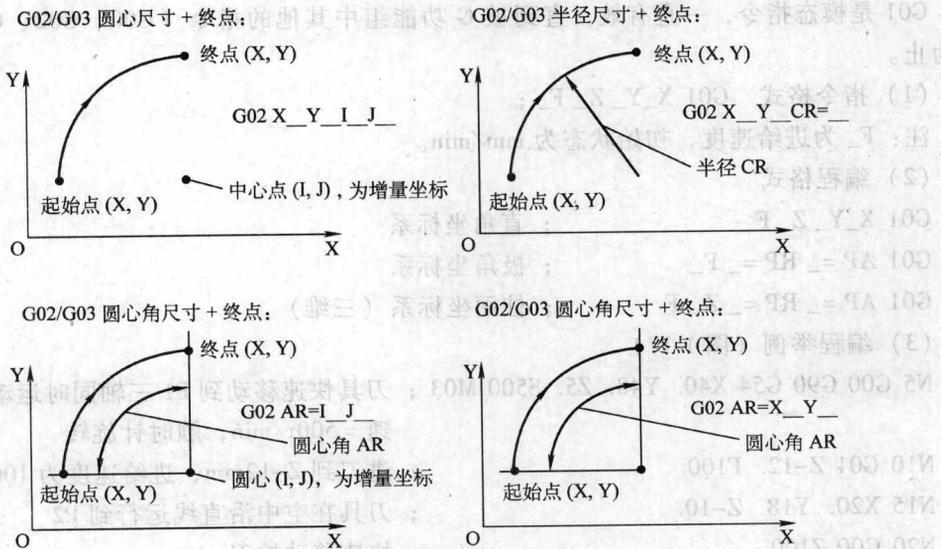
用 G02/G03 圆弧编程的方法 (举例: X/Y 轴)
